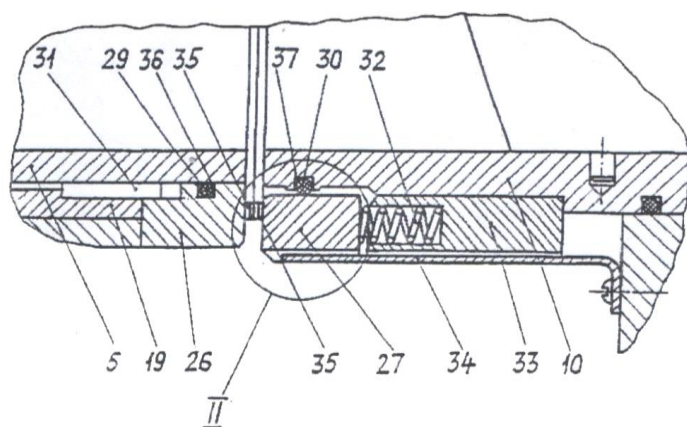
Вузол пружновстановленого ущільнювального кільця торцевого ущільнення статора турбіни: 26, 27 – ущільнюючі кільця; 29, 30 – ущільнення; 31 – порожнина; 32 – пружина; 33 – основа пружного елемента; 34 – фіксатор; 35 – контактна поверхня робочих торців ущільнювальних кілець; 36 – канавка
